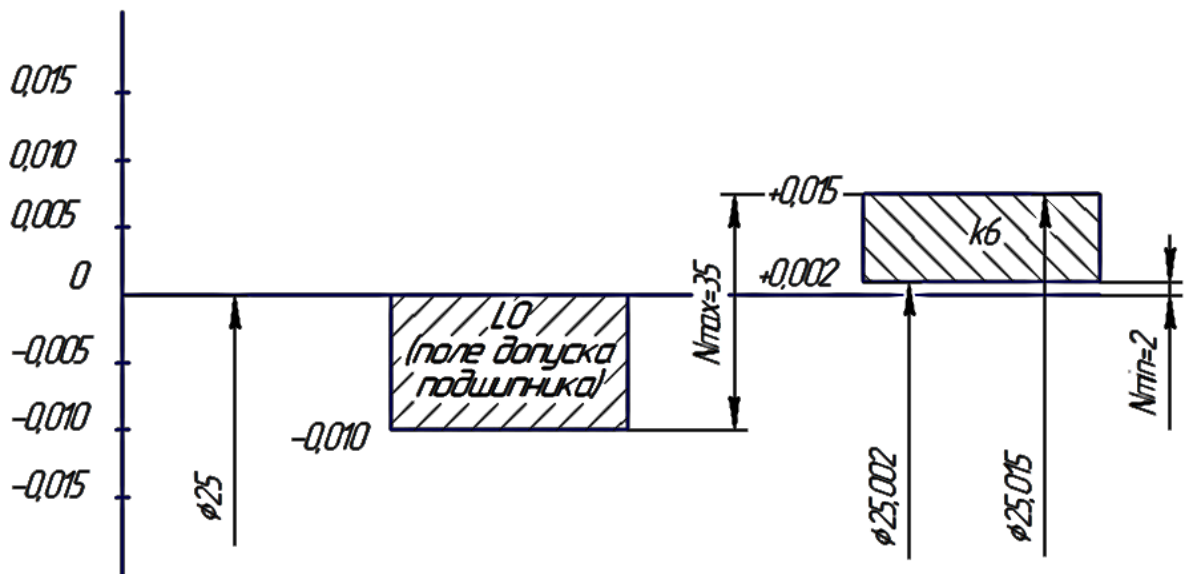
Графическое изображение полей допусков подшипника и вала.
